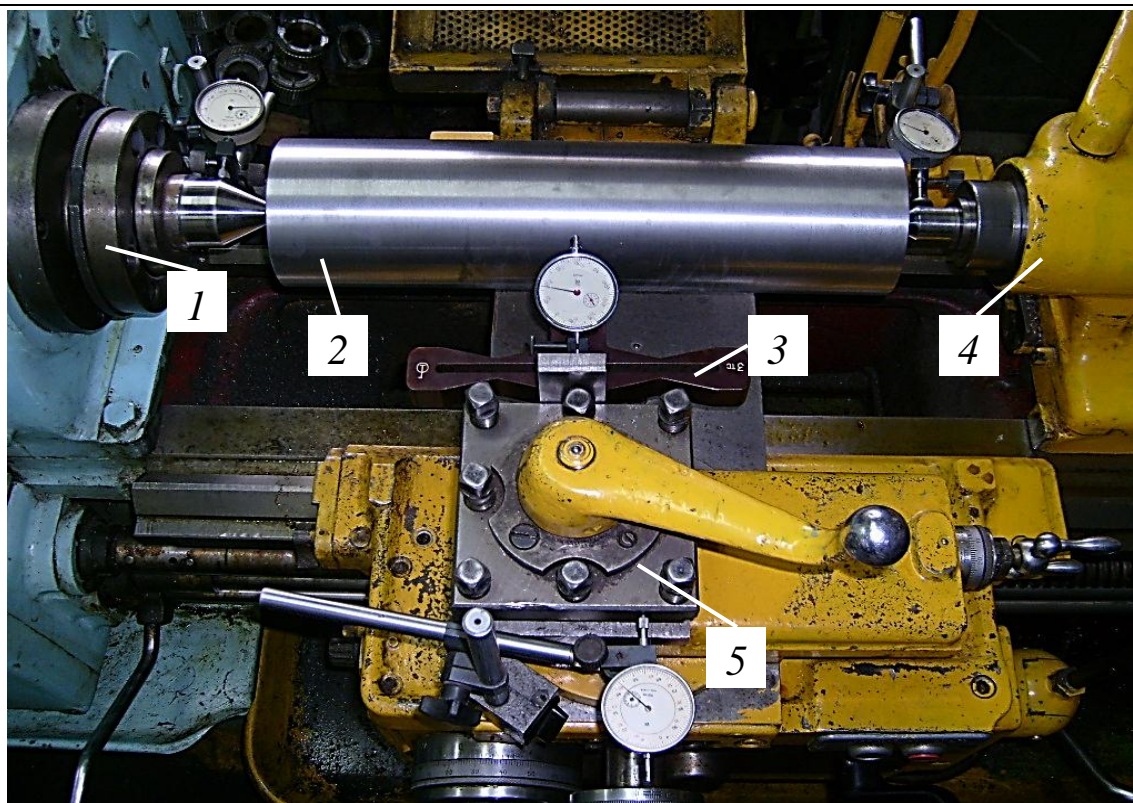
Установка для измерения податливости токарного станка при обработке заготовки в центрах: 1 – передняя бабка; 2 – заготовка; 3 – динамометр ДОС-3тс; 4 – задняя бабка; 5 – резцедержатель.
